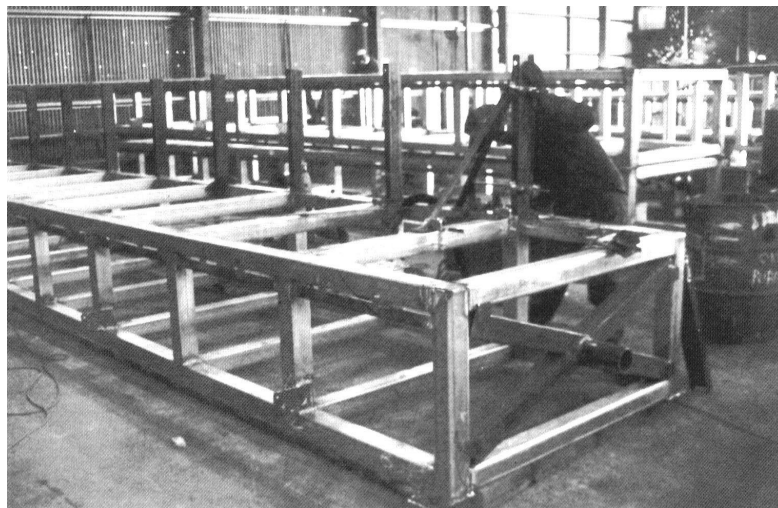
Dispositivo para soldagem de estrutura em perfis
